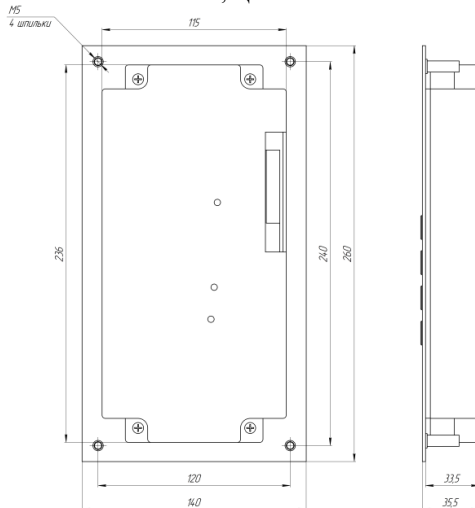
Установочные и габаритные размеры блоков вызова
